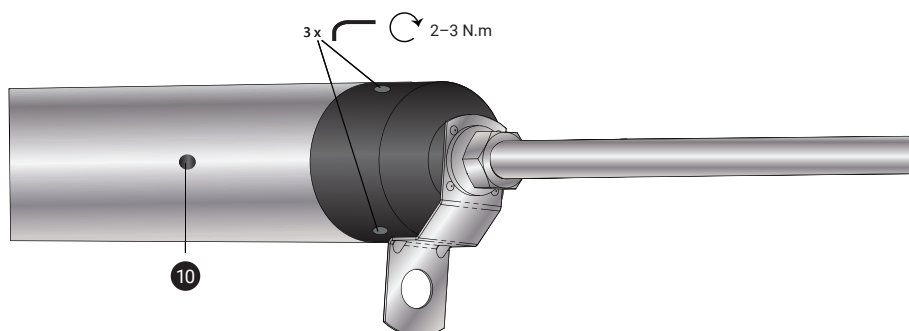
Serrare il coperchio del palo sull'assemblaggio del palo superiore
